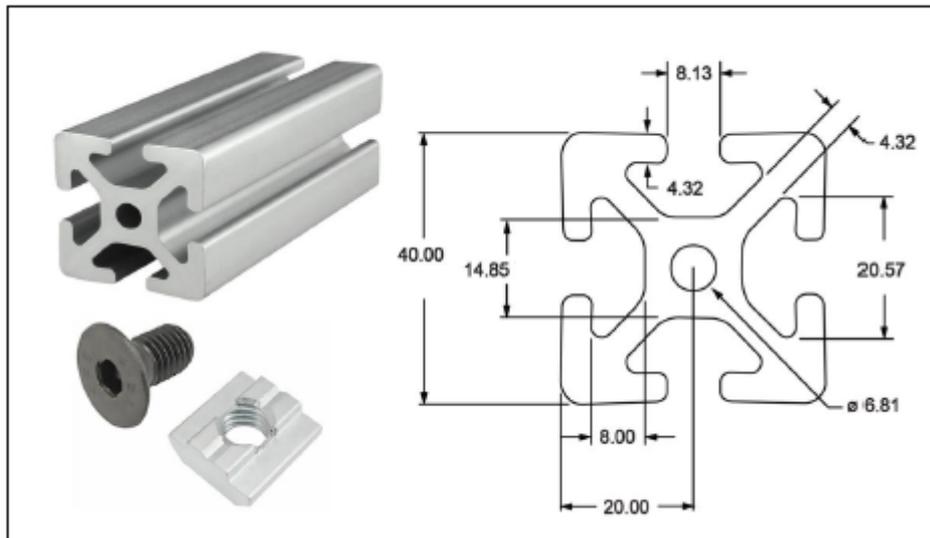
Sporgenza per montaggio carico utile, dimensioni in mm e dado a T
